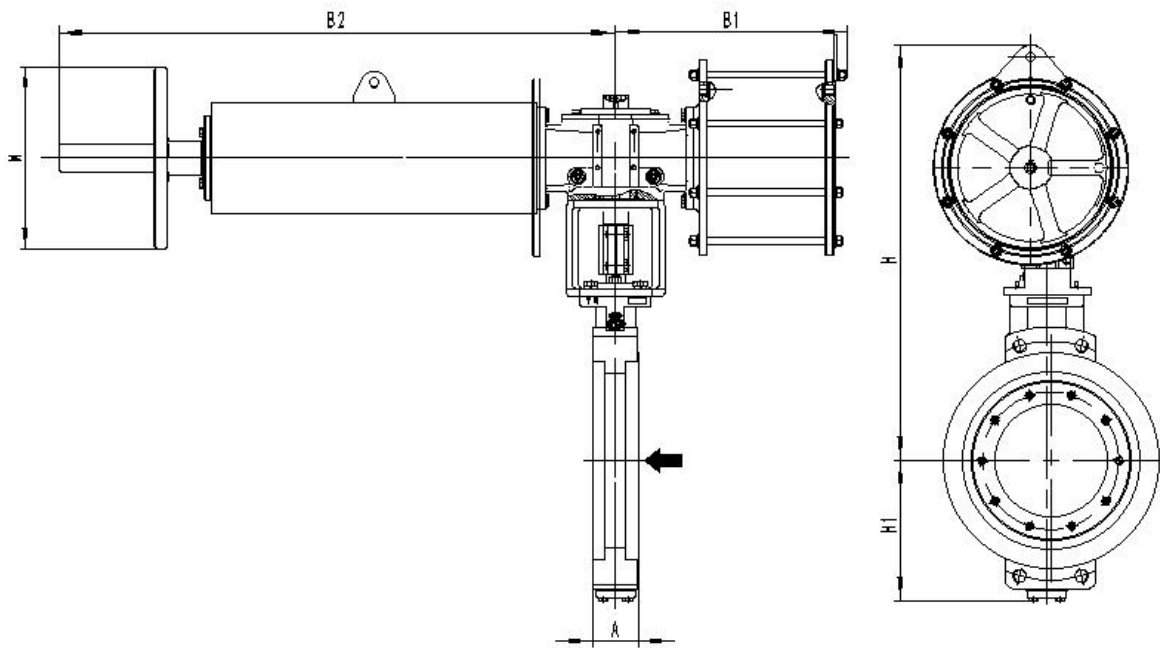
配 AW18SD41~AW27SD52 带丝杆手轮外形尺寸图(FO 此状态为执行机构通气状态)
